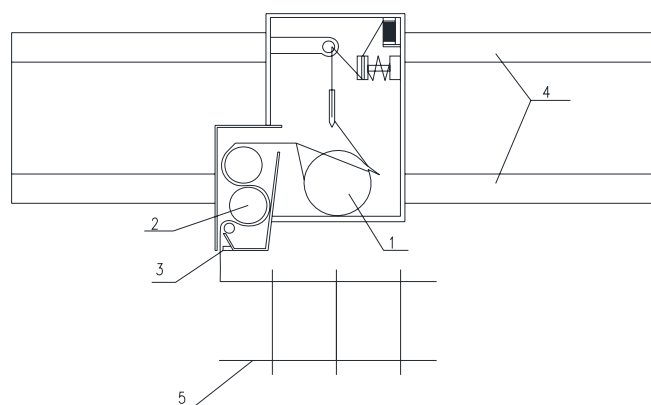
3D-принтер, печатающий волокнистым композитом:
